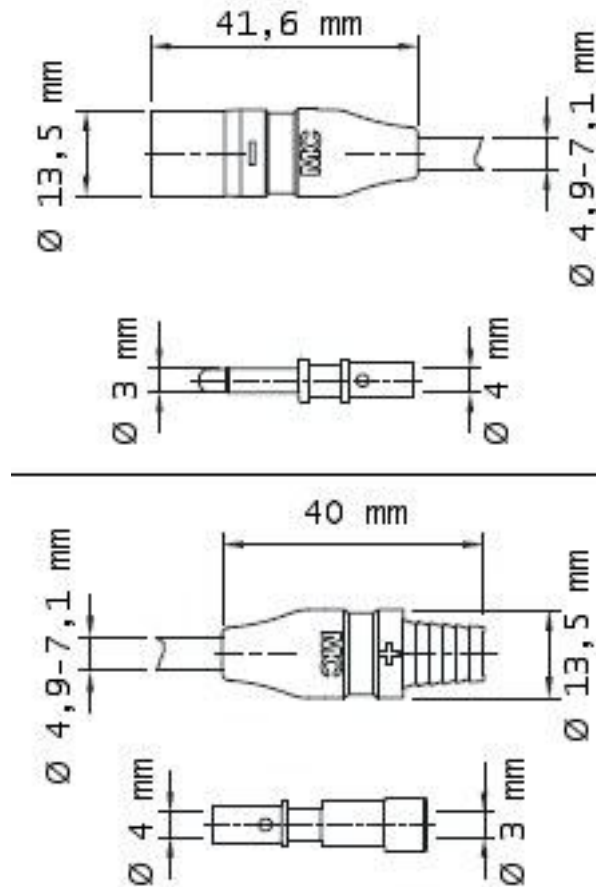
Dimensioni dei componenti del connettore MC3.[18]
